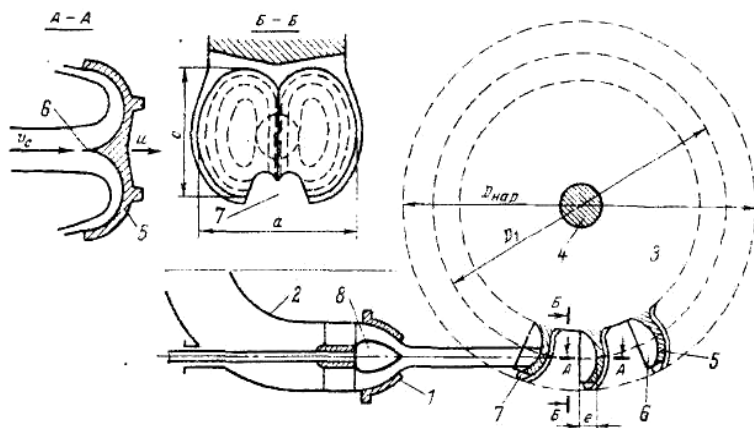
Схема ковшовой турбины: 1 – сопло; 2 – трубопровод; 3 – рабочее колесо; 4 – вал; 5- лопасть турбины; 6 – нож; 7- прорезь; 8 – игла.
